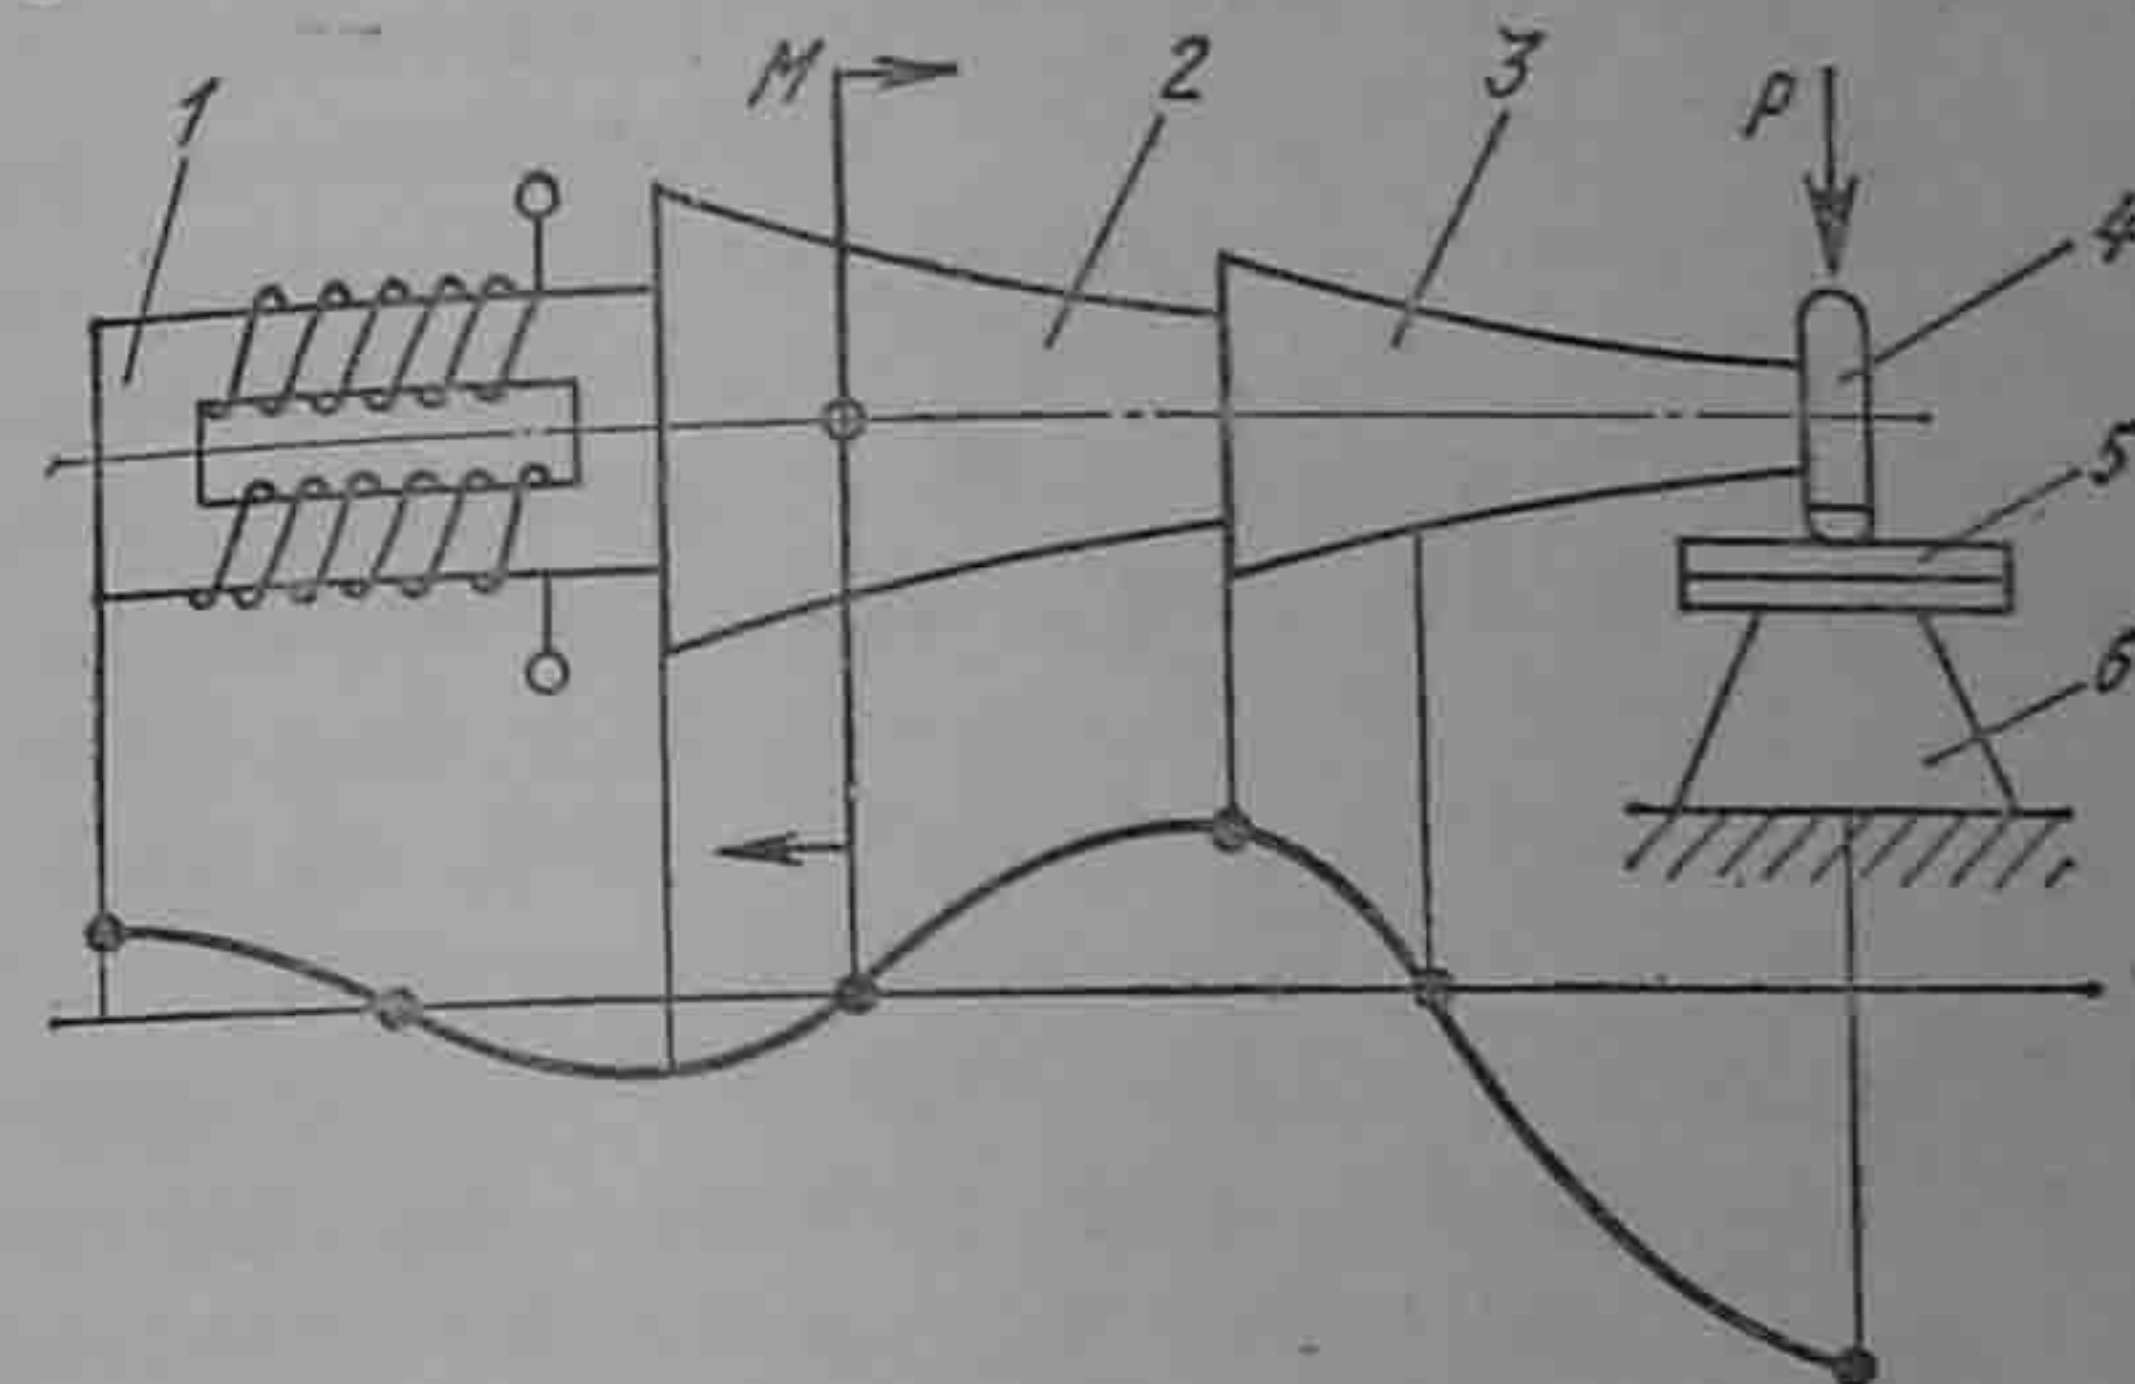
Принципиальная схема ультразвуковой сварки
